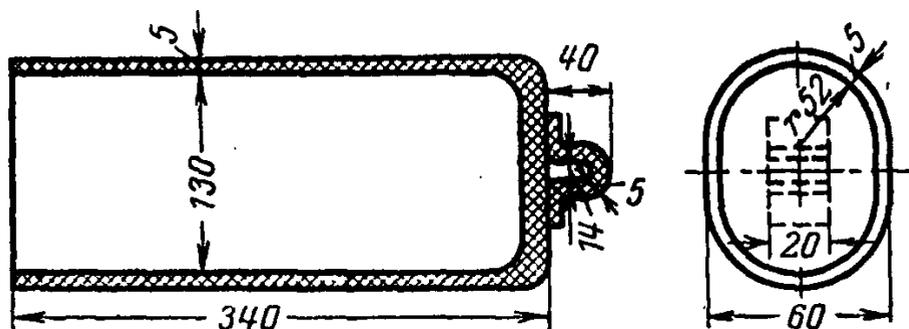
Изолирующий резиновый колпак для однополюсного разъединителя 10 кВ
